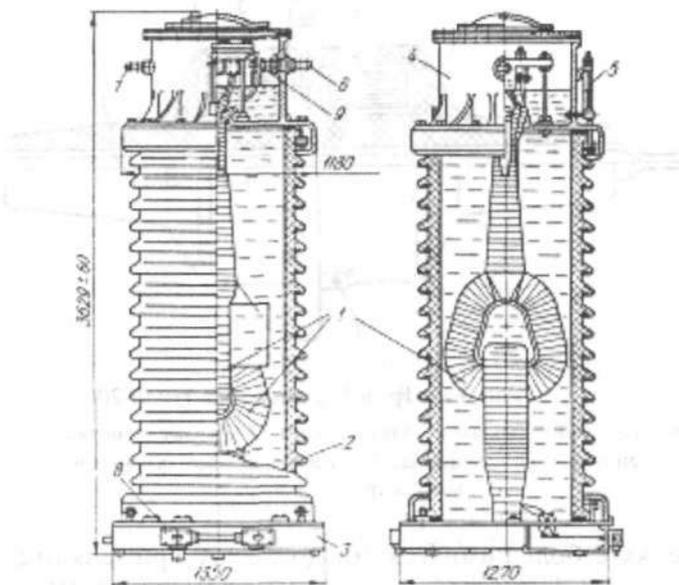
Внешний вид и разрез трансформатора тока ТФН-220 на 220 кВ:
